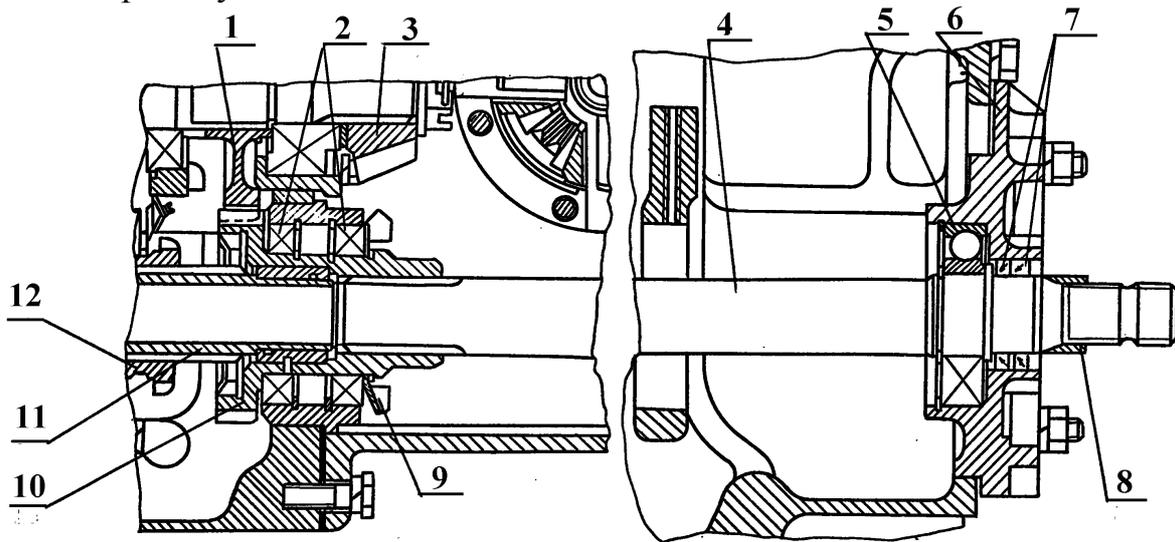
Привод от КПП к приводу заднего моста: 1 – ведомая шестерня II ступени редуктора; 2, 5 – подшипники; 3 – ведущая шестерня главной передачи; 4 – вал; 6 – крышка; 7 – манжеты; 8 – втулка; 9 – крыльчатка; 10 – ведущая шестерня II ступени редуктора и привода заднего моста; 11 – промежуточный вал; 12 – ведущая шестерня I ступени редуктора
